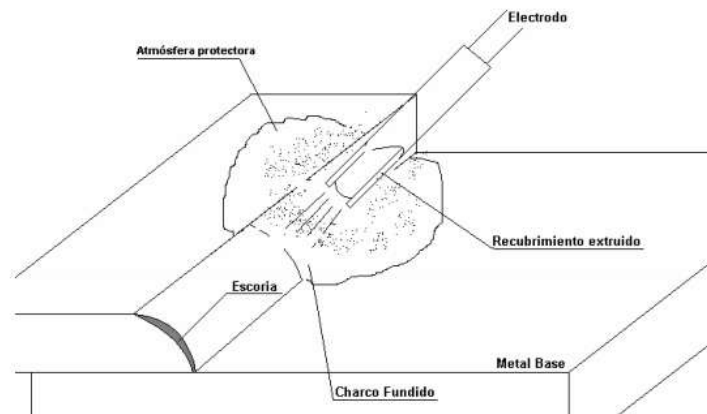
ESQUEMA DEL PROCESO DE SOLDADURA SMAW
